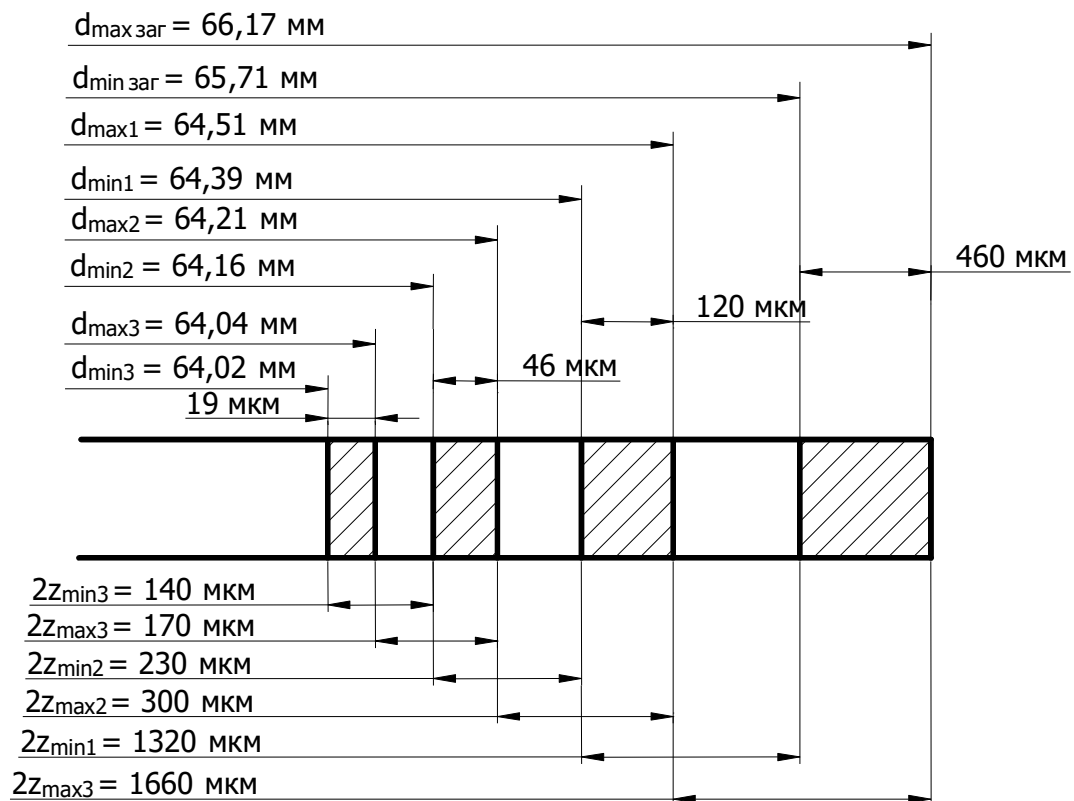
Схематичне зображення розміщення припусків та допусків на поверхню деталі $\varnothing 64 \text{ h7}$.
